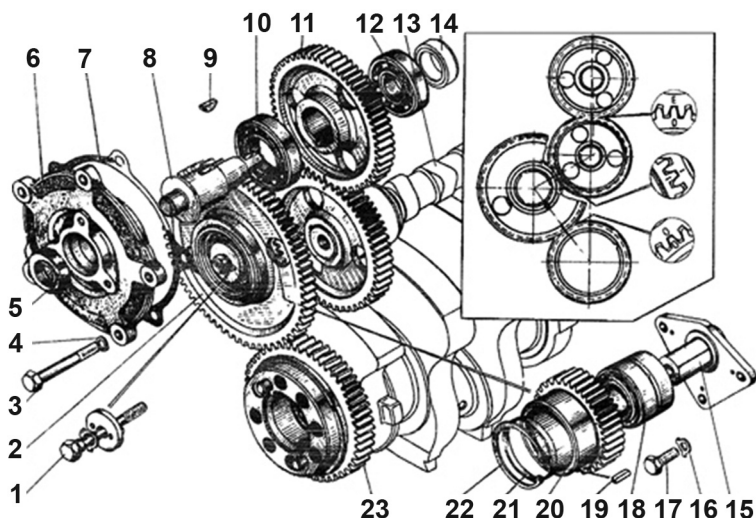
Привод агрегатов (двигатель без картера агрегатов):
